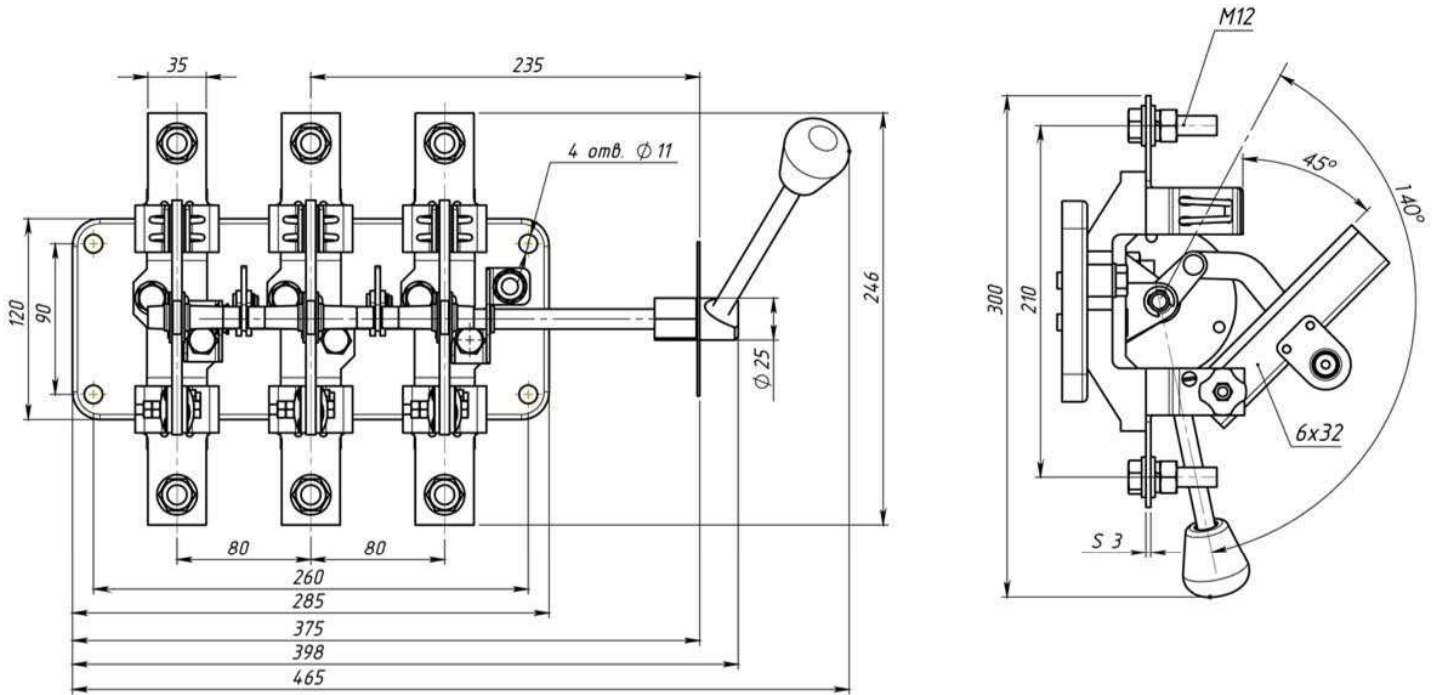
Разъединитель серии P с боковой рукояткой РБ-6, на номинальный ток 630 А
